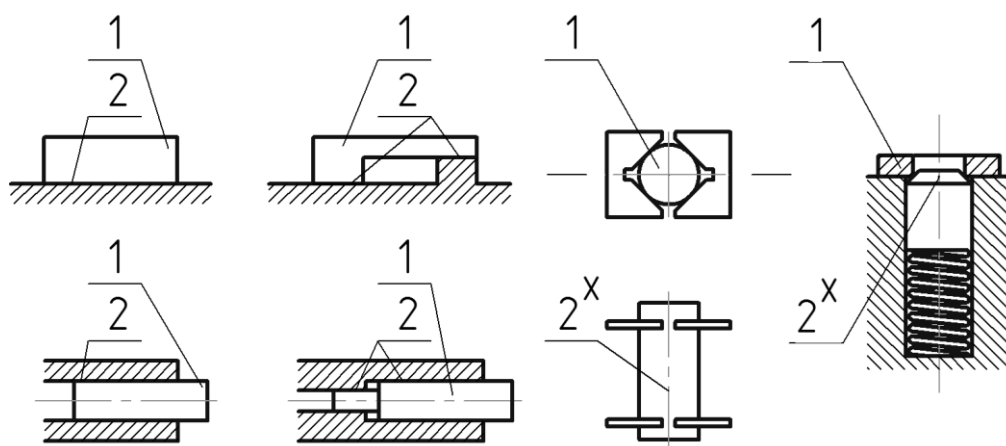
Виды баз: 1 — заготовка, 2 — база
